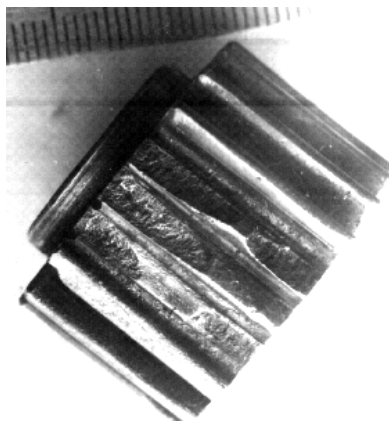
Поломка зубьев шестерни топливного насоса двигателя «Шкода» с землесоса «1005» из-за наличия цементитной сетки
